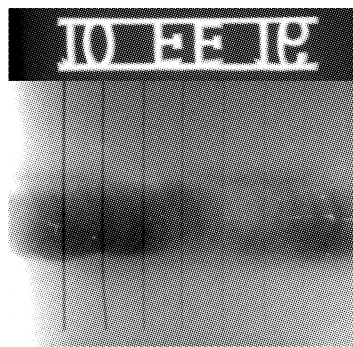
焊缝质量 B 级测试的 DR 图像
